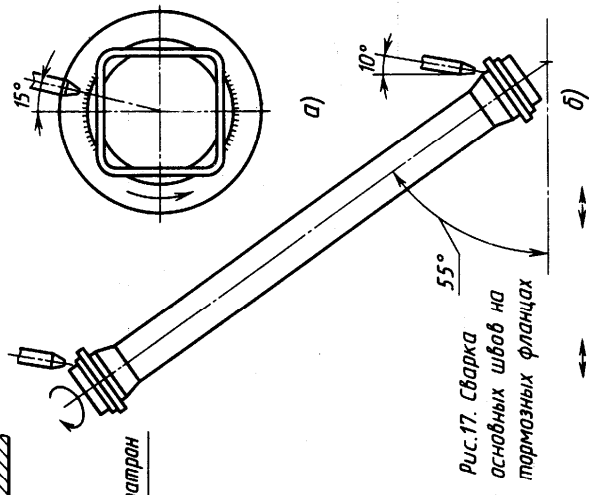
Сварка основных швов на тормозных фланцах
